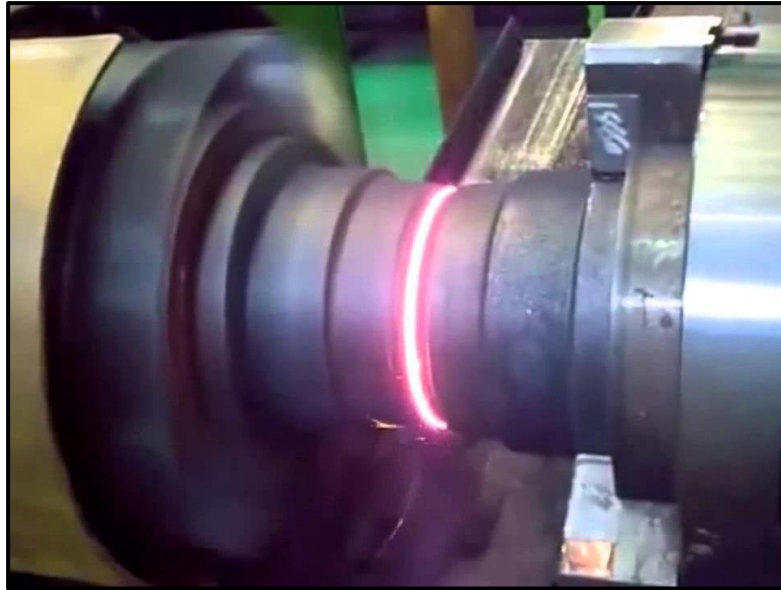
Soldadura por fricción. fuente:Youtube canal de Aioros Dokho
